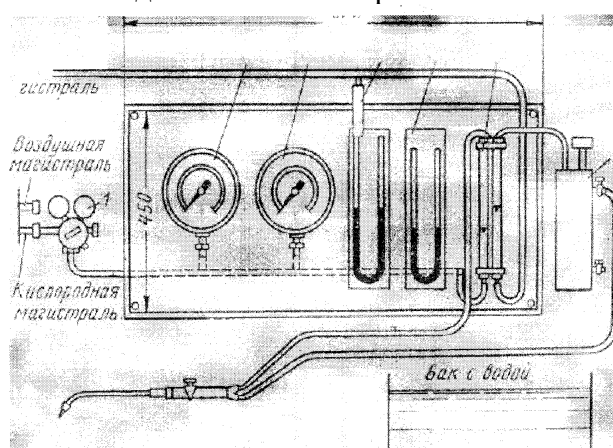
Стенд для испытания горелок и резаков:
